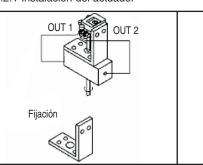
Montaje mediante el tornillo ateral del posicionado
